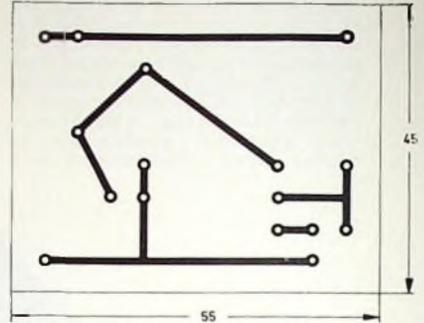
Printplatte für die Schaltung im Bild 2 (Maßstab 1:1)
